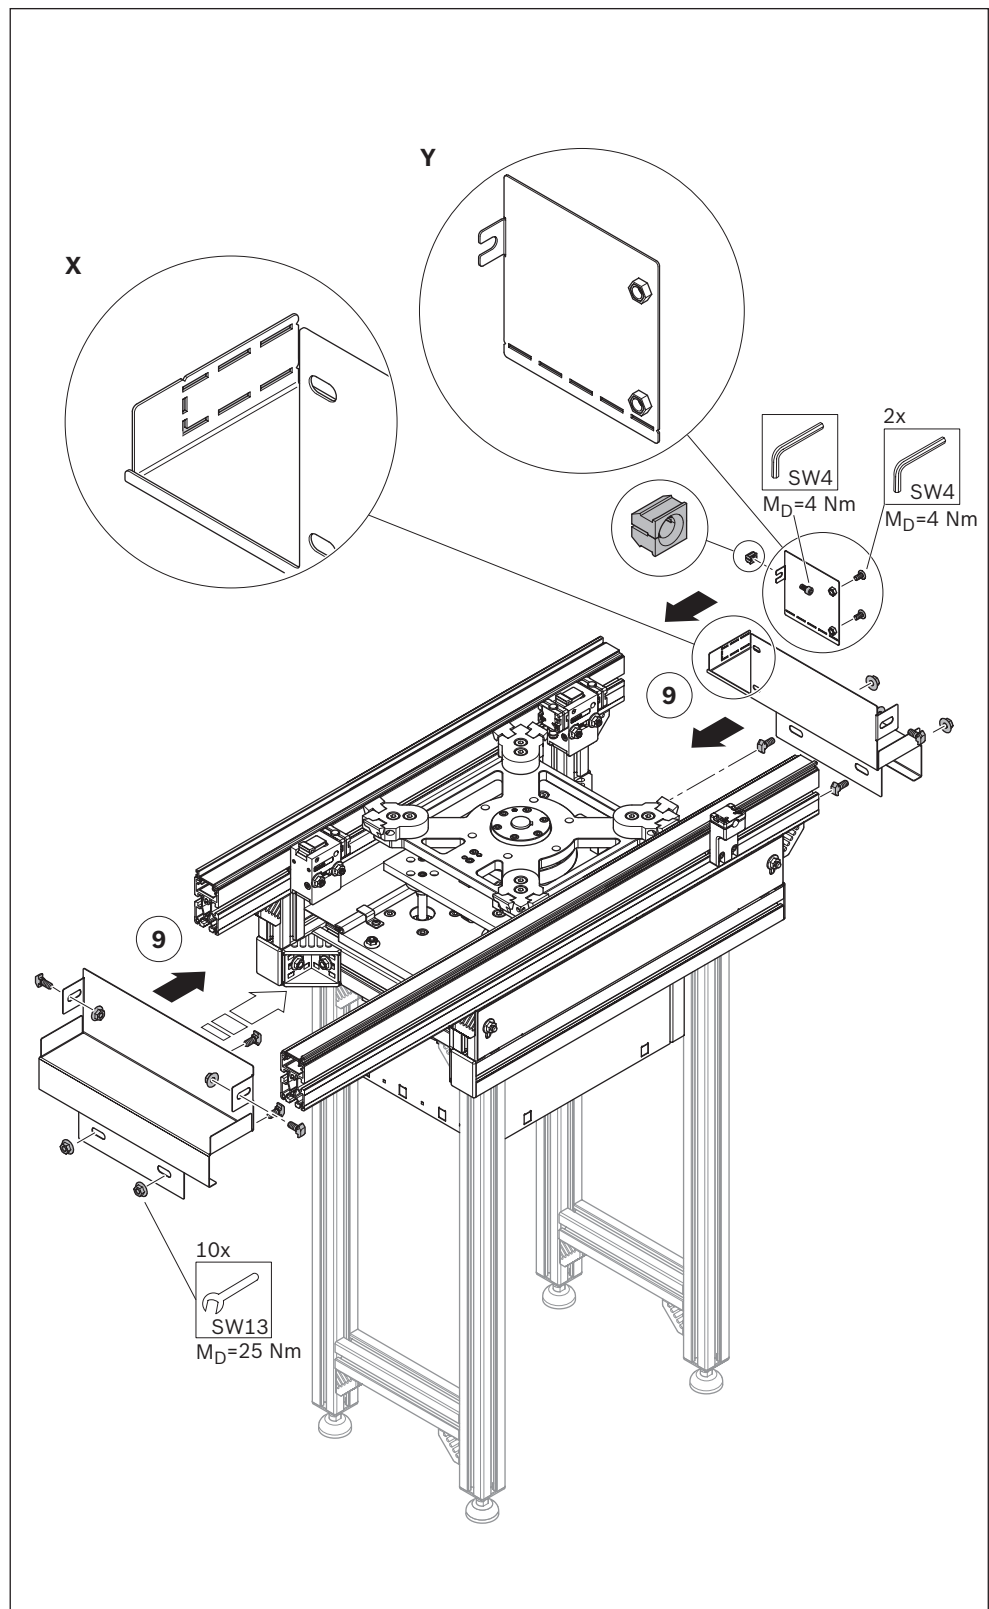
Montaje de las chapas de protección laterales (aquí tamaño constructivo 2 180° para WT 2, WT 2/F)
